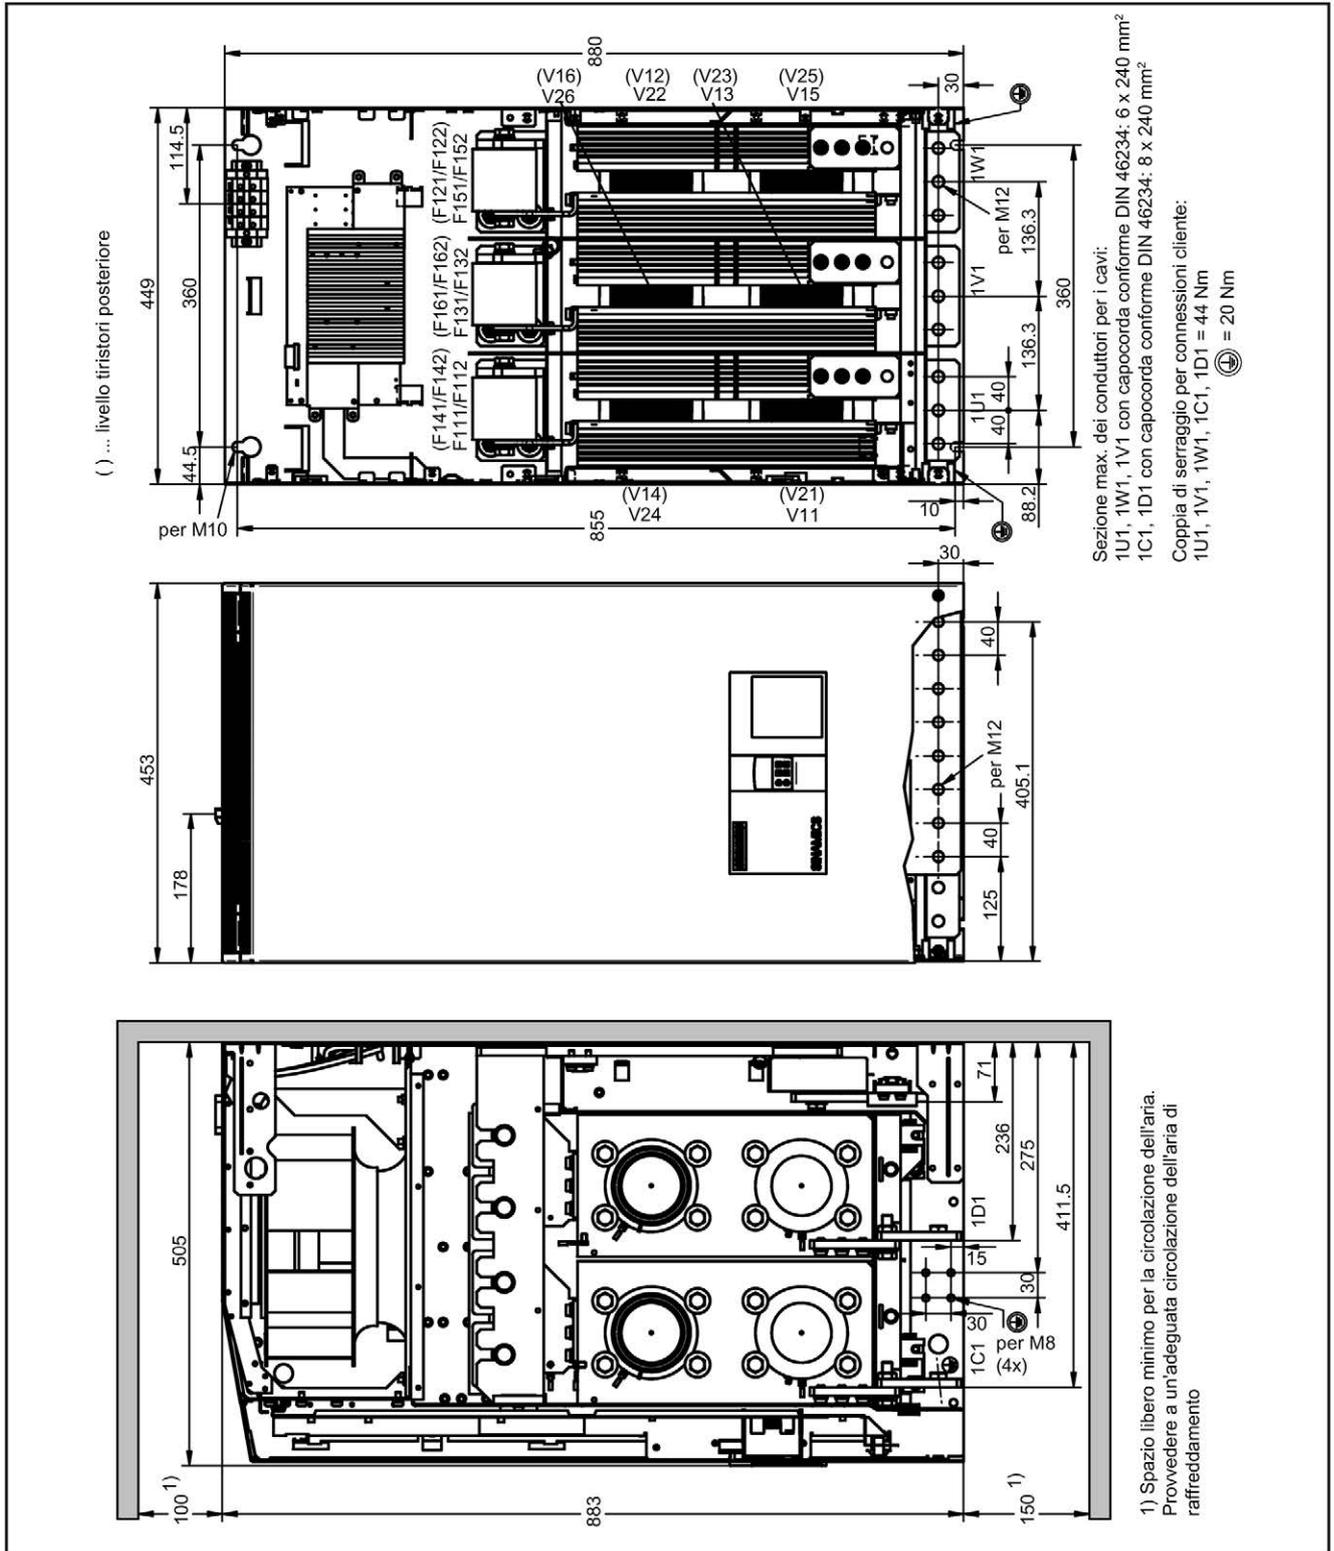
Disegno quotato 1500 A ... 3000 A
